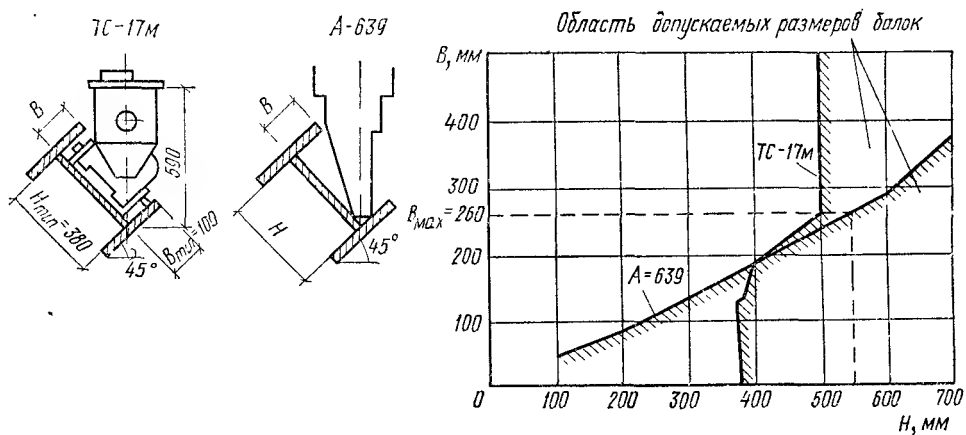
Размеры двутавровых сечений, допускающие сварку трактором ТС-17м и сварочной головкой А-639
